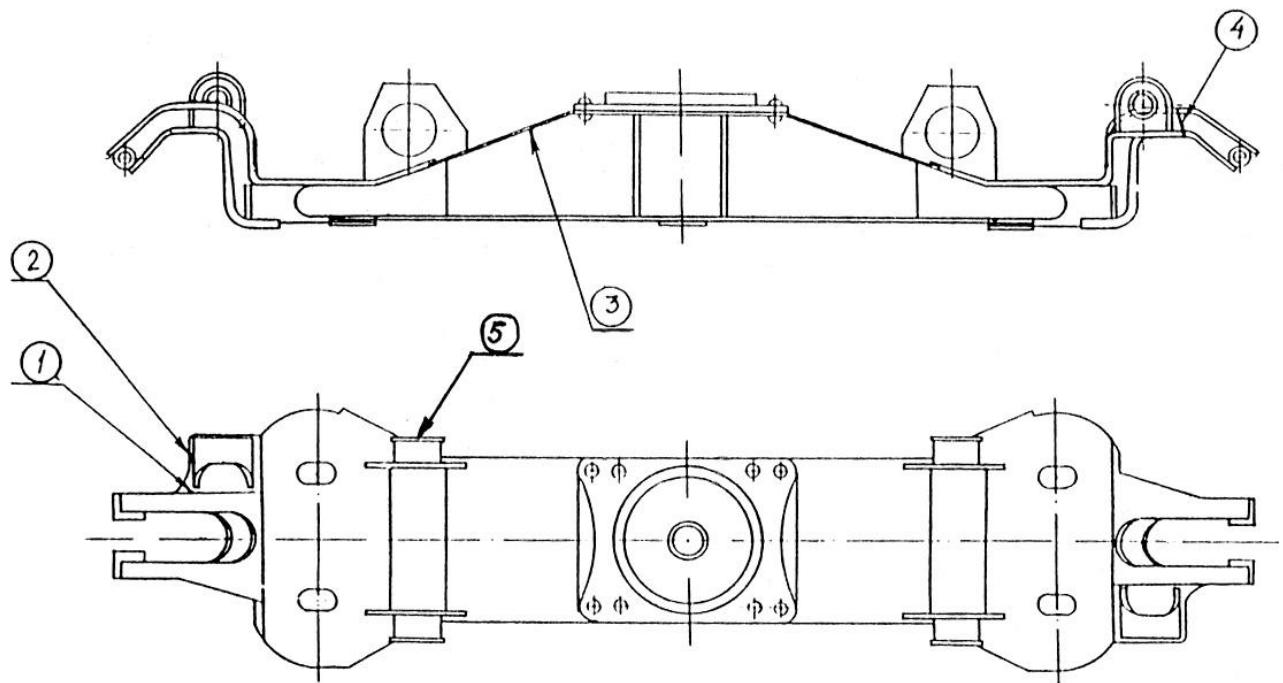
Основные дефекты балки надрессорной тележки КВЗ-ЦНИИ, ремонтируемые сваркой или наплавкой
